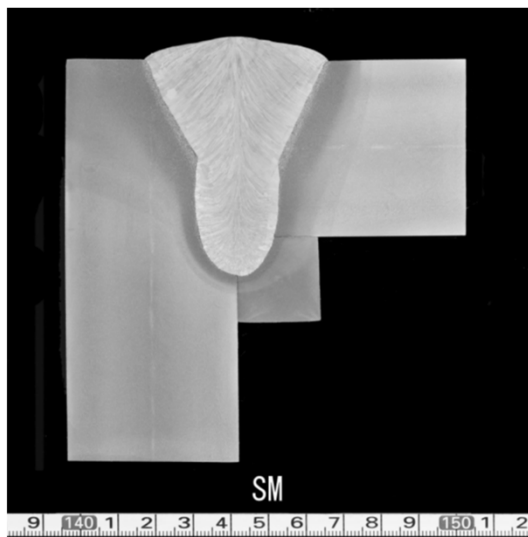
サブマージアーク溶接マクロ(板厚45mm)
